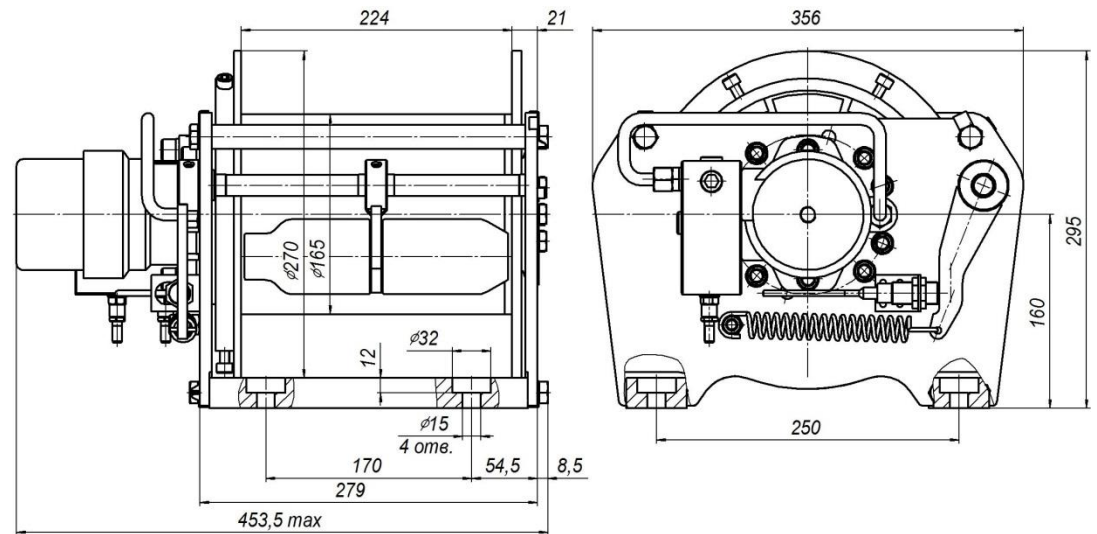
Общий вид, габаритные и присоединительные размеры
